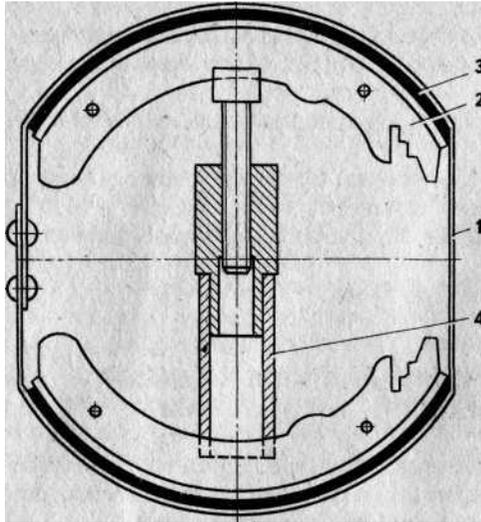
Приспособление для приклейки накладок тормозных колодок:
